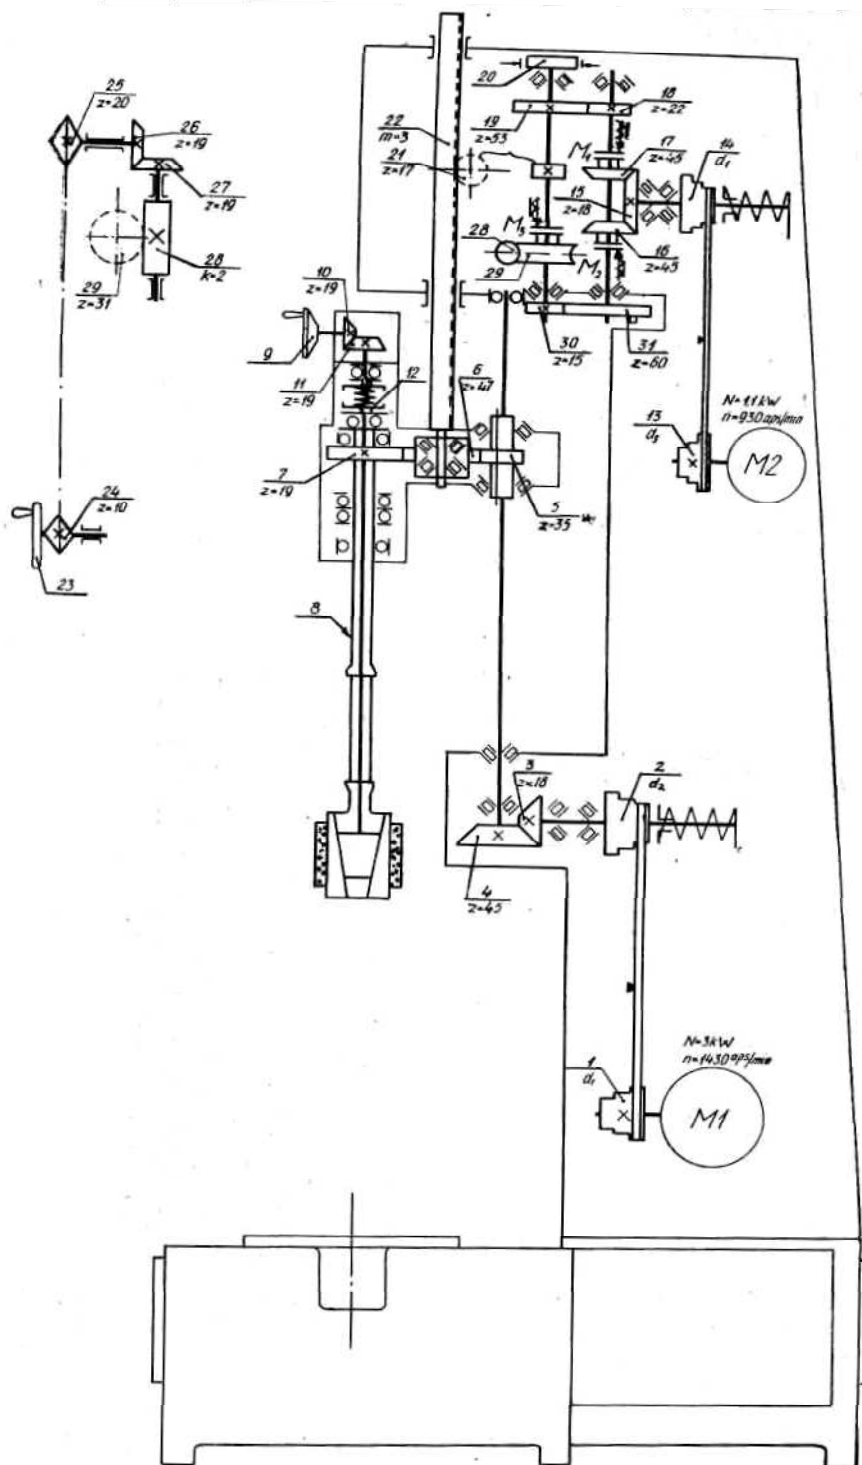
Кинематическая схема хонинговального станка модели 3Г833
